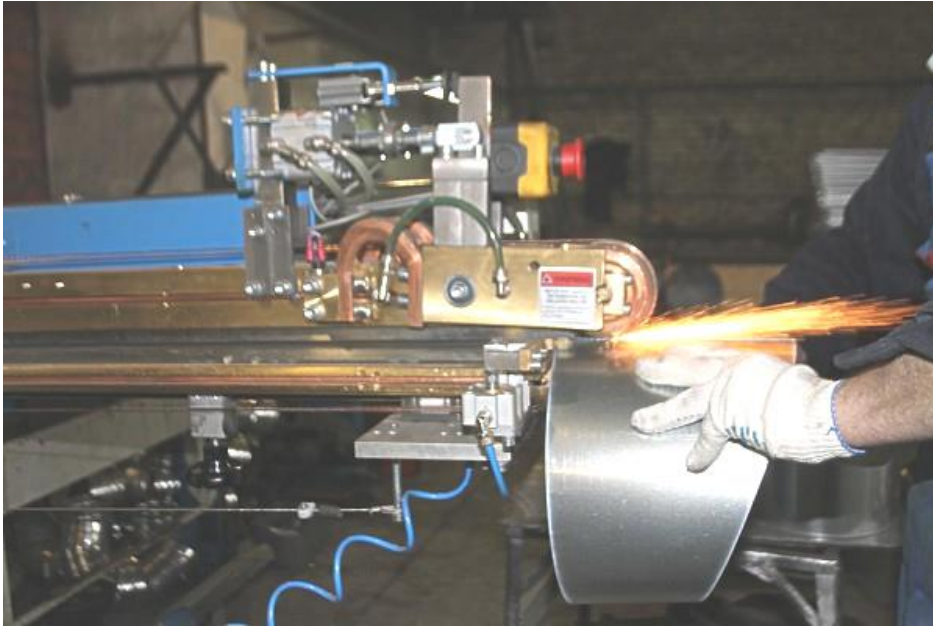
Загальний вигляд процесу шовного зварювання
